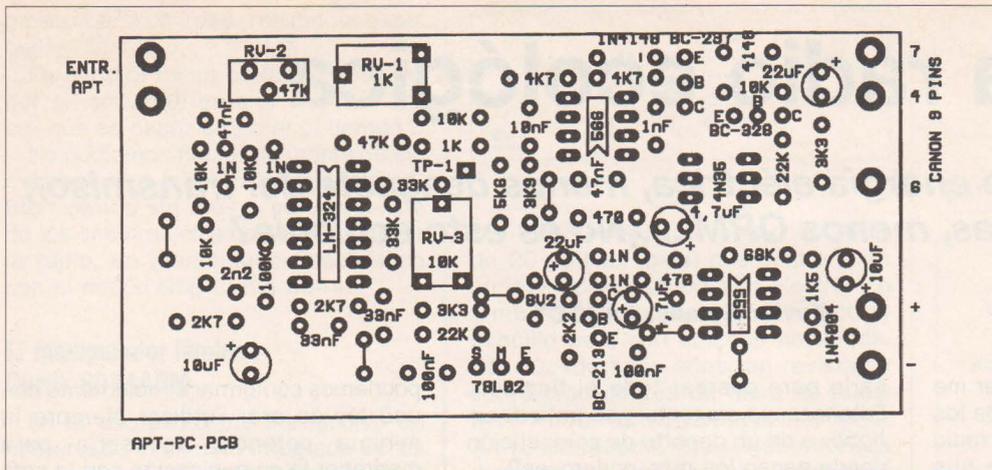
Disposición de componentes en la placa de circuito impreso.
